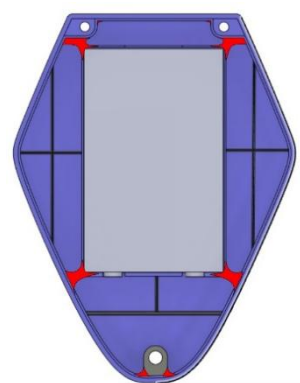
Разработка внутренних элементов конструкции нижней части корпуса
